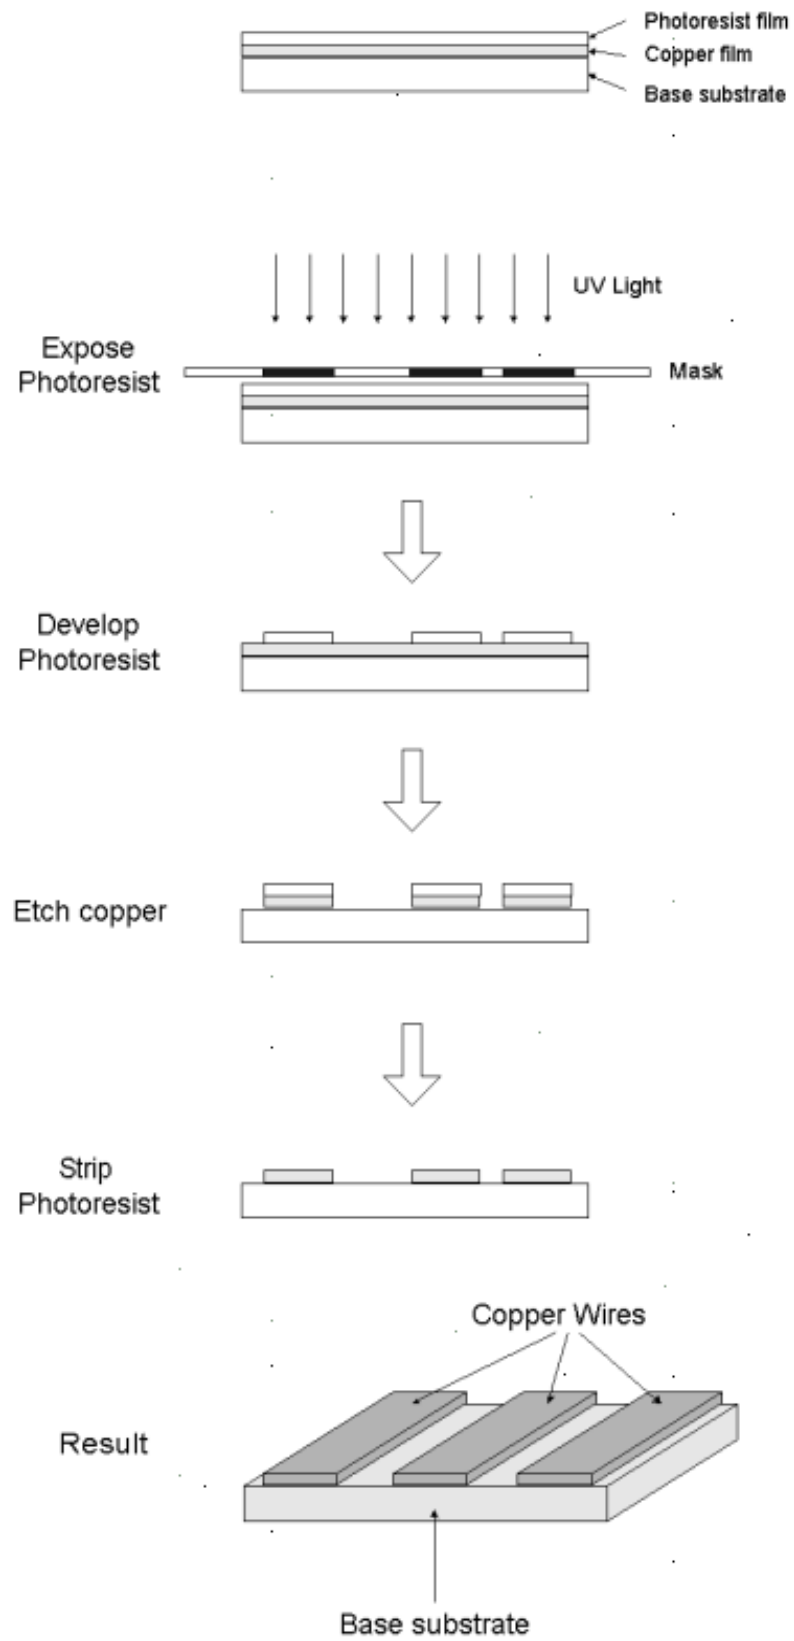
乾膜光阻應用於 PCB 製程示意圖
